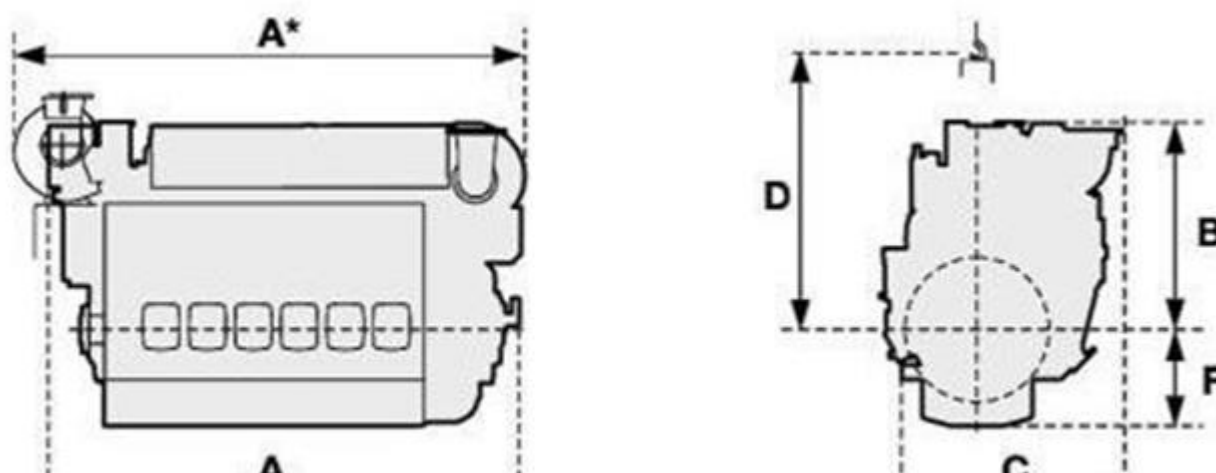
Габаритные присоединительные размеры двигателя «Wartsila 20DF»
